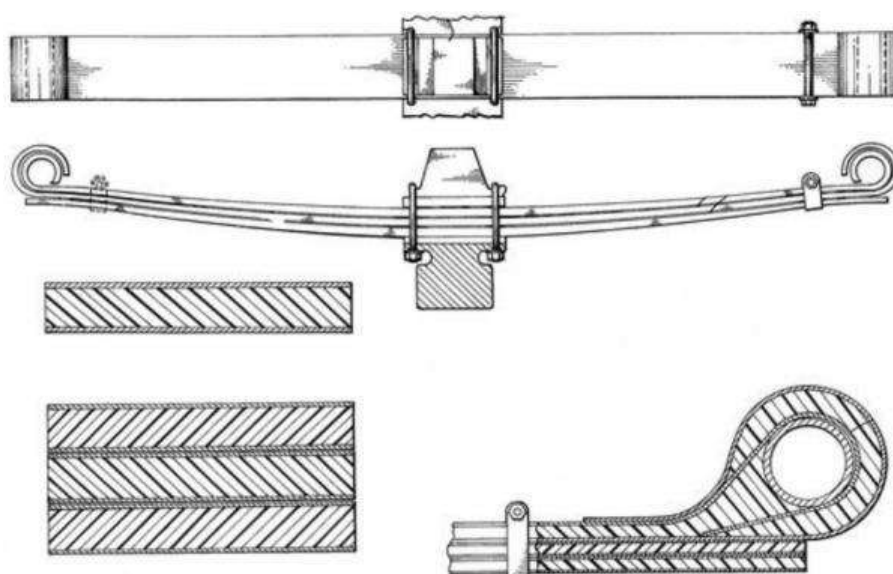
Конструкція багатолистової ресори з ПКМ, форсованої сталевими листами
